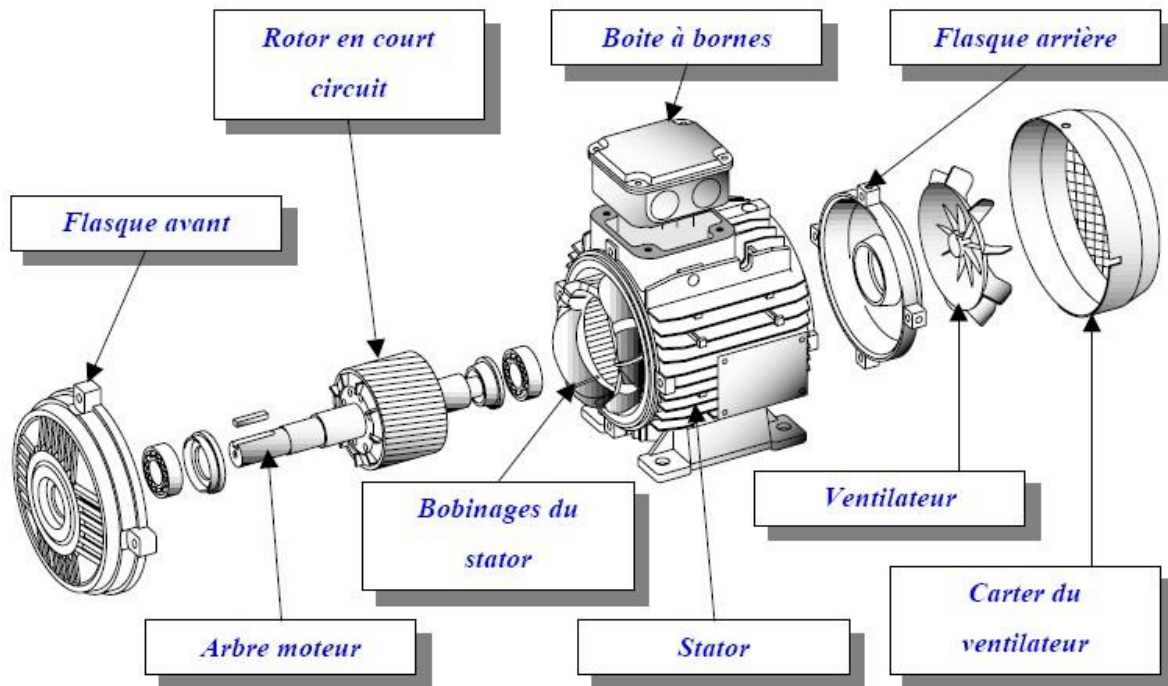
13 -Vue éclatée de la machine asynchrone. [10]
